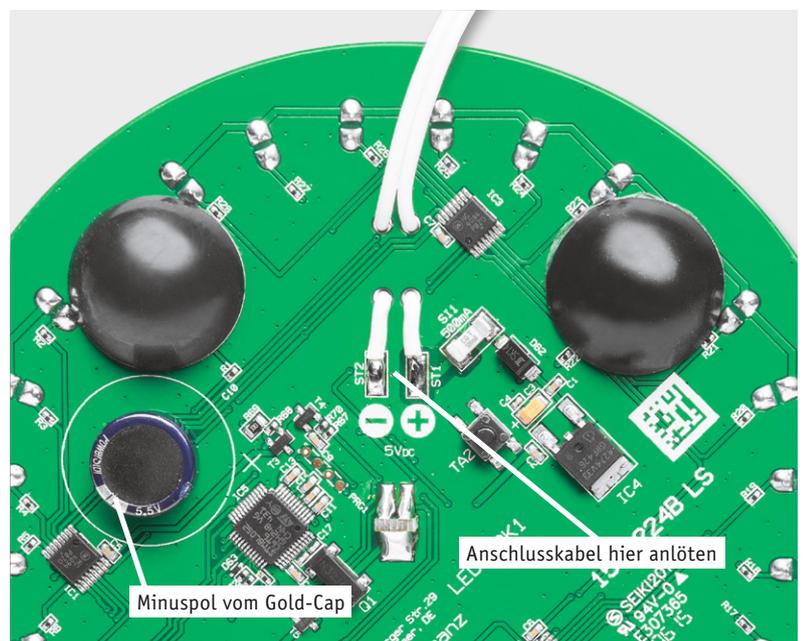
Blick auf die Unterseite der Schaltung. Hier sind die richtige Einbaulage des Gold-Caps sowie Führung und Anschluss der Stromversorgungsleitung zu sehen.
